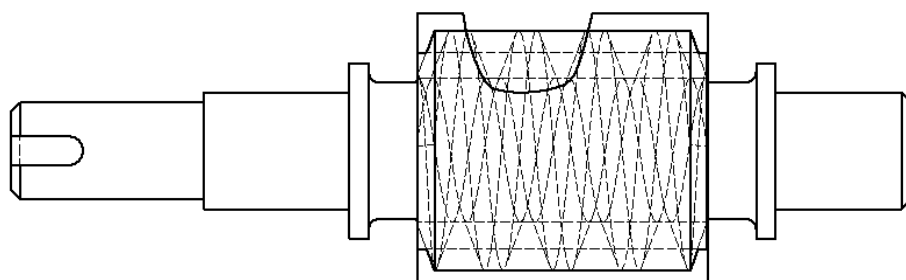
1-й місцевий розріз, деталь – циліндричний черв'як
